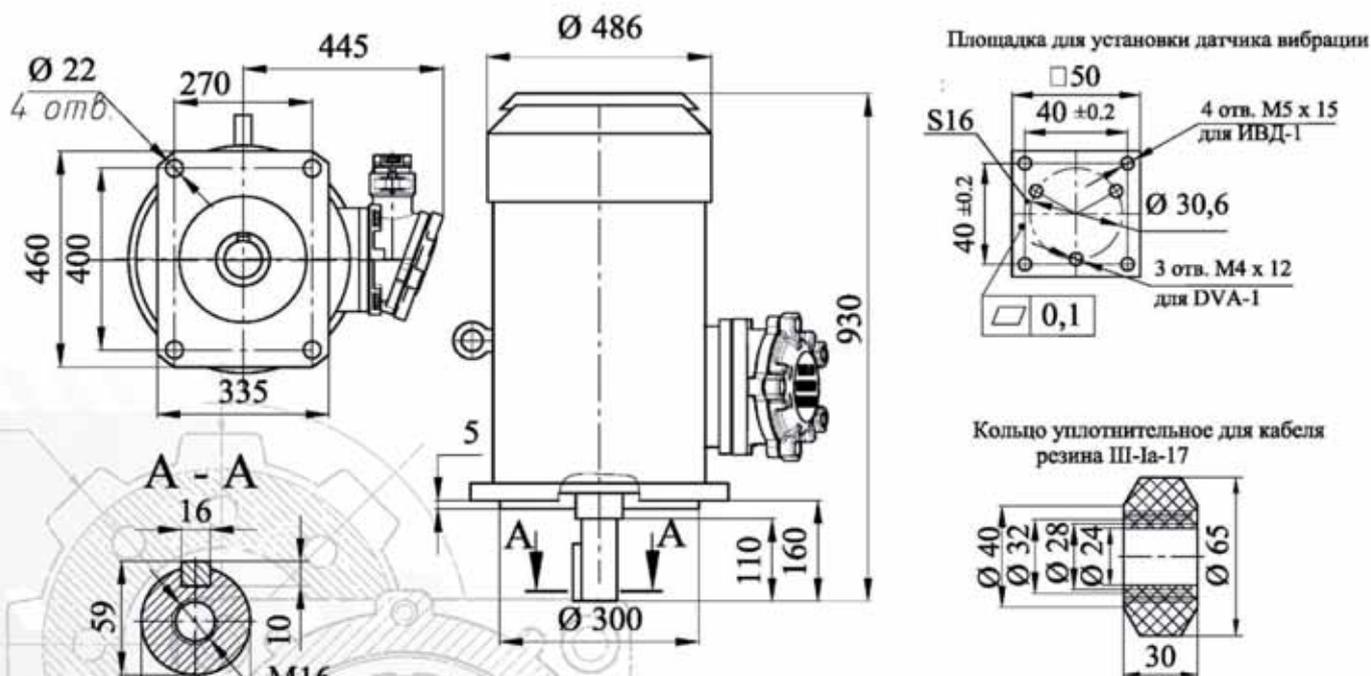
Габаритные и установочно-присоединительные размеры АИММ225М12У1, IM3081
